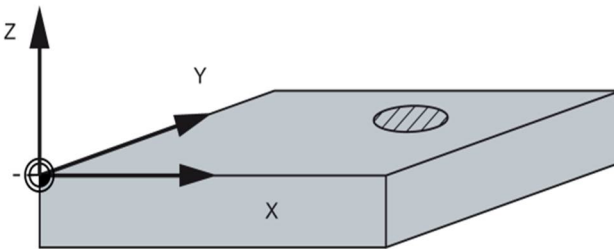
Розташування нульової точки заготовки при роботі на фрезерному верстаті з ЧПК
